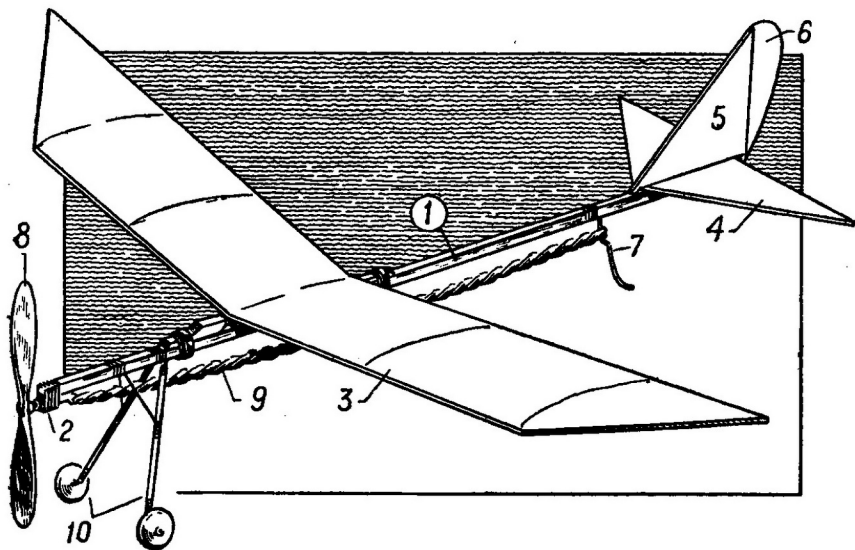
Общий вид схематической модели самолета с резиновым мотором:
